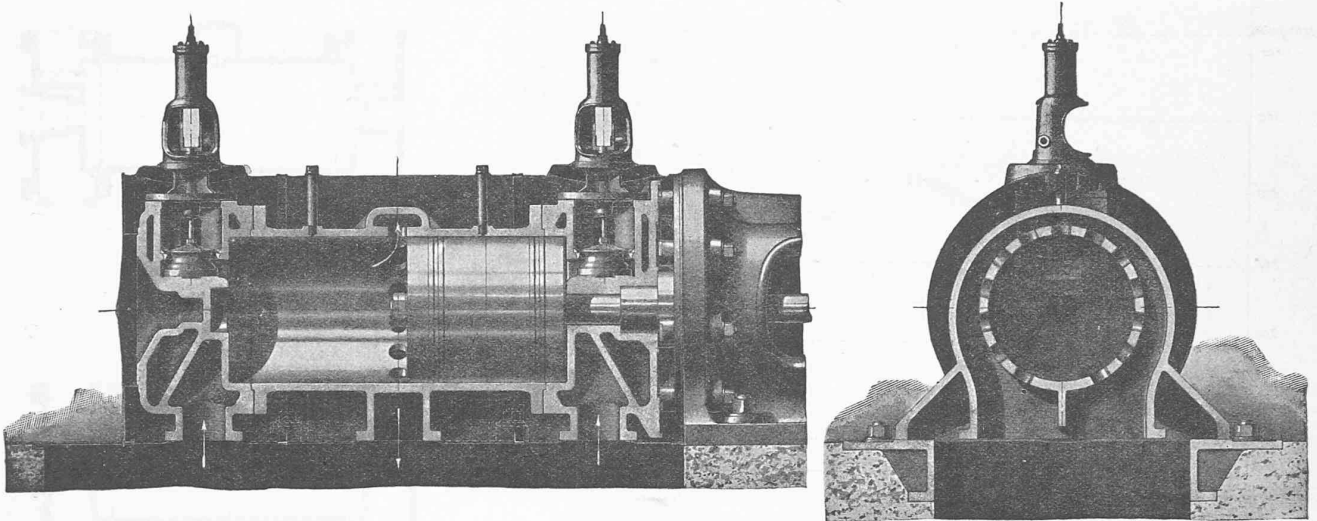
Coupe du cylindre d'une machine à flux continu de Sulzer frères.
